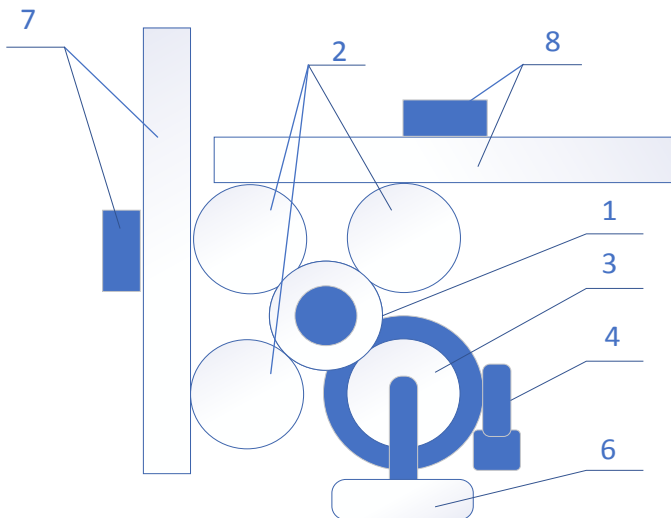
Схема базового механізму поворотного столика для мікроскопа: 1 – серцевинна шестерня; 2 – основні шестерні; 3 – поворотно-приводна шестерня; 4 – кроковий двигун; 5 – корпус основного стола мікроскопа (виноскою не показаний); 6 – фіксатор поворотного столика; 7, 8 – рухомі планки з фіксаторами координатного поля
